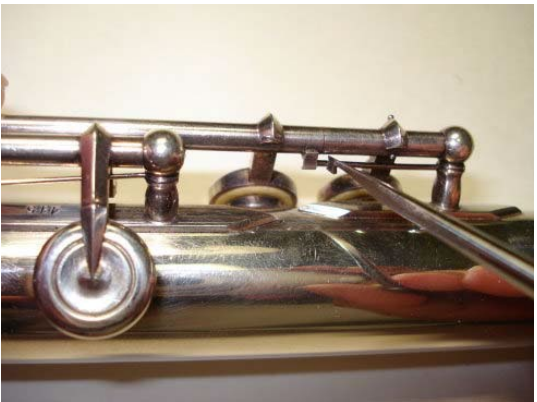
Пружину клапана Pe. Трельный клапан обозначается здесь красной стрелкой.
